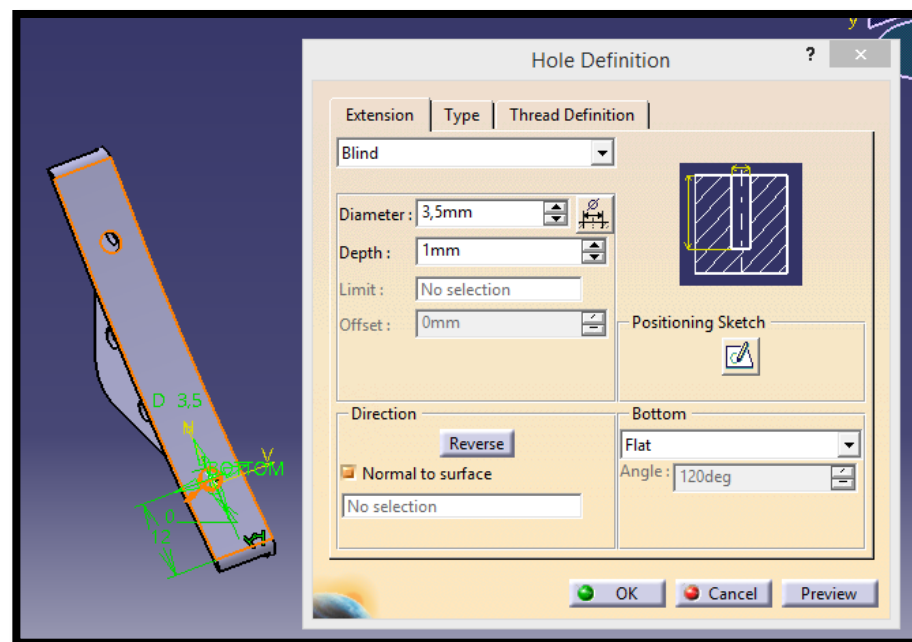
Seat mounting frame 11: Hole.2 sujeción inferior 1
